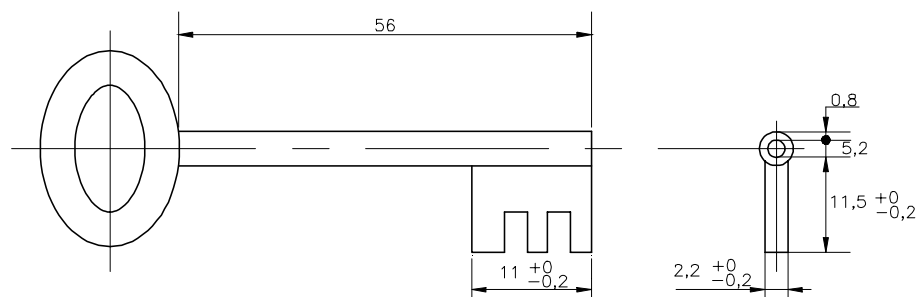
Chave para fechadura de sector – desenho EDP n.º E84-004-03 (dimensões a fornecer ao adjudicatário)
